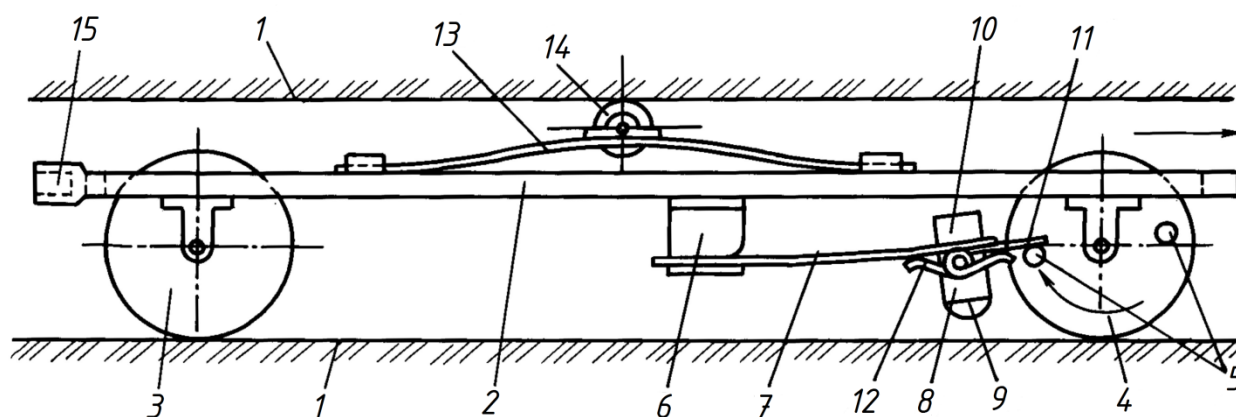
Устройство в позиции исследования шпура в момент начала цикла взвода ударника. 1-исследуемый шпур; 2-монтажная рама; 3-концевой ролик; 4-обрезиненный приводной ролик; 5-взводные штифты; 6-основание для крепления плоской пружины; 7-плоская взводная пружина; 8-ударник; 9-боек; 10-электромеханический преобразователь; 11-двусторонняя собачка; 12-пружина собачки; 13-прижимная рессора; 14-прижимной ролик; 15-хвостовик.
